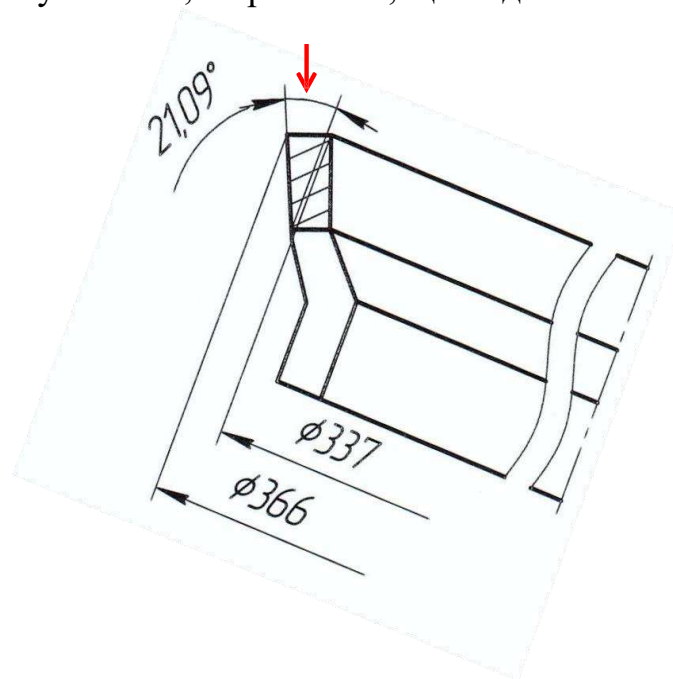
Схема наплавлення 5-ї ділянки
